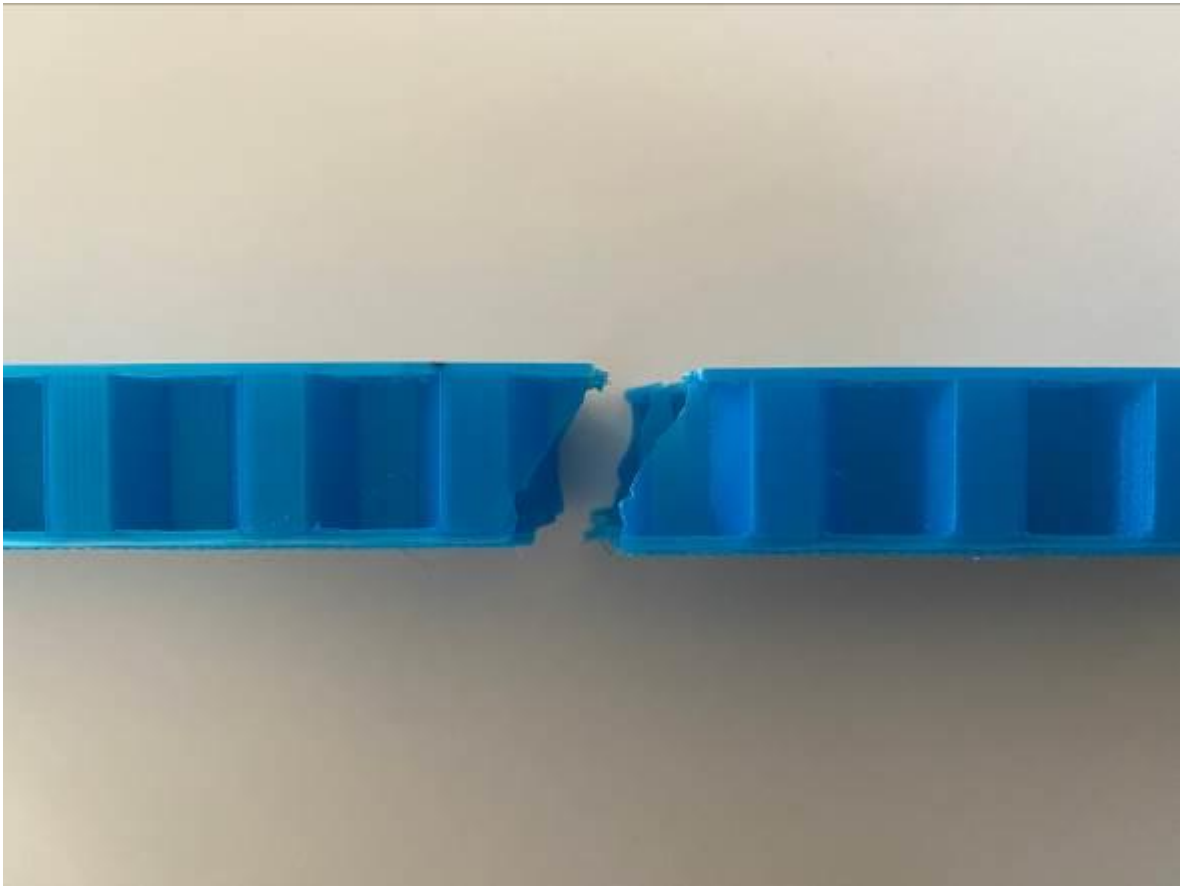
Espécimen 4 del lote de 3/8" fabricado completamente en PLA; tipo de falla X-A-F.
